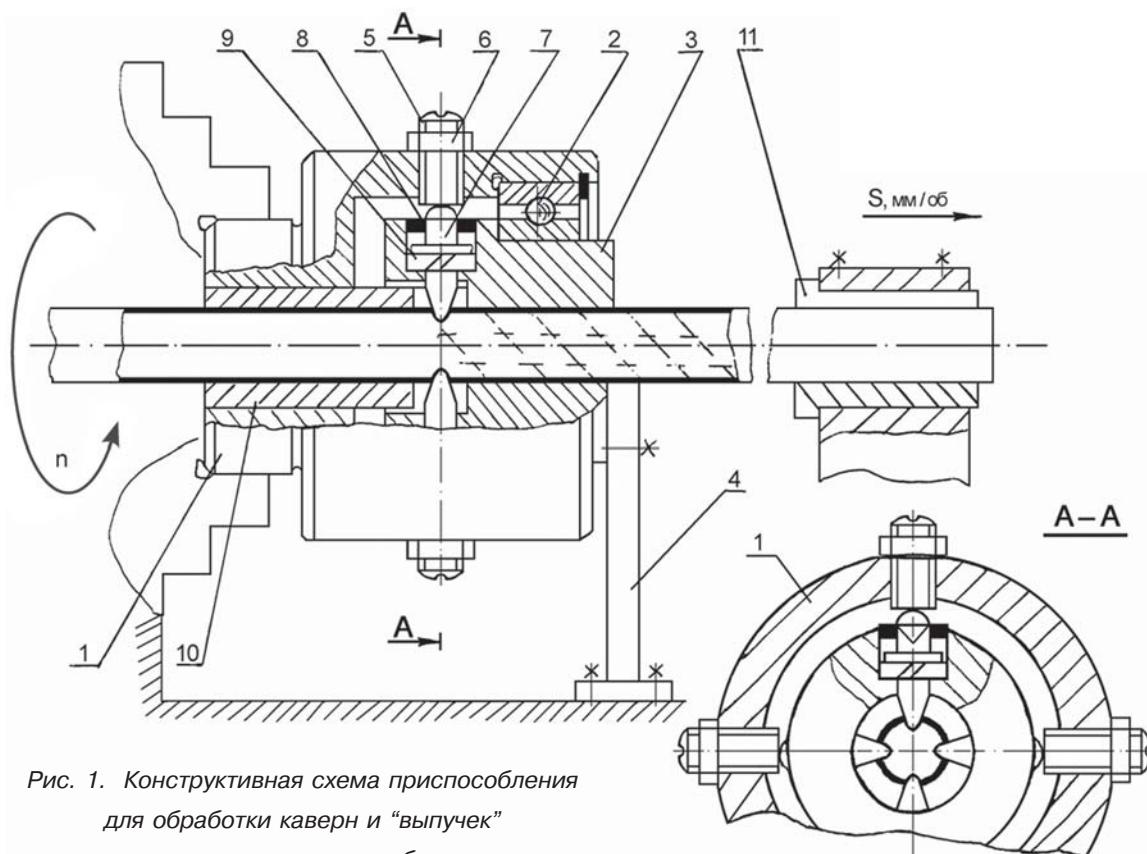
Конструктивная схема приспособления для обработки каверн и «выпучек» на тонкостенных трубах
